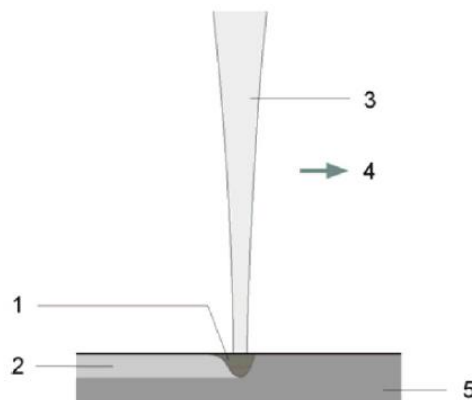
Princípio de Funcionamento da Soldadura por Condução de Calor: 1 – Material Fundido; 2 – Cordão de Soldadura; 3 – Feixe *Laser*; 4 – Sentido de Avanço; 5 – Peça a Soldar [63].
